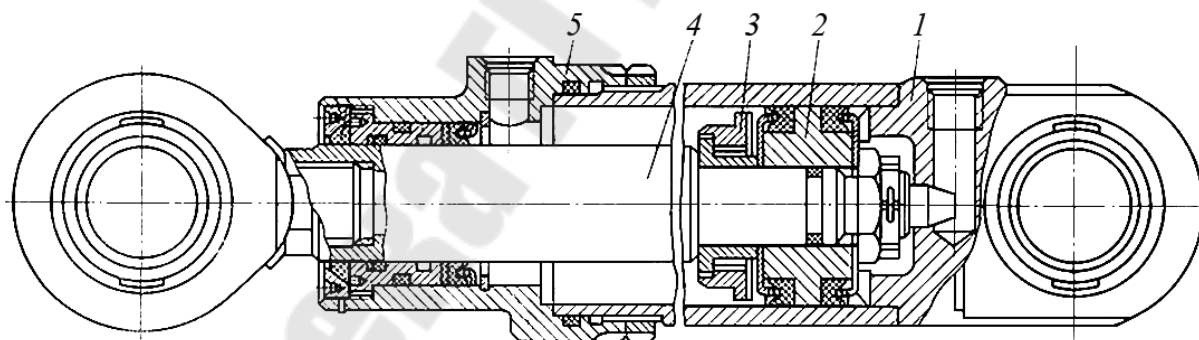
1. – Конструкция поршневого цилиндра с двумя рабочими полостями
